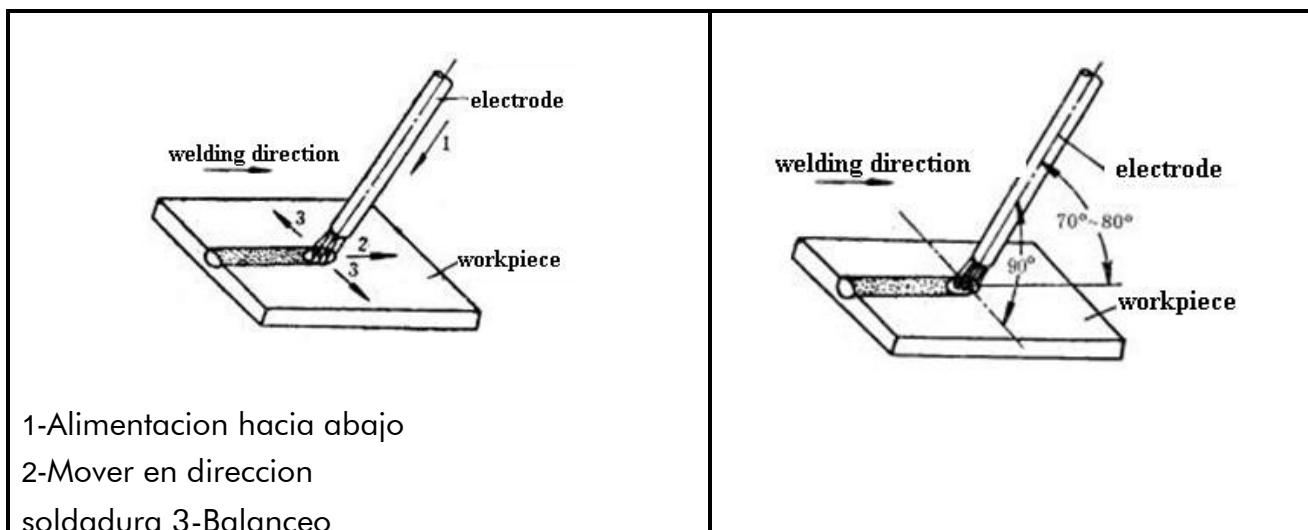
Tres direcciones básicas movimiento electrodo en soldadura plana
